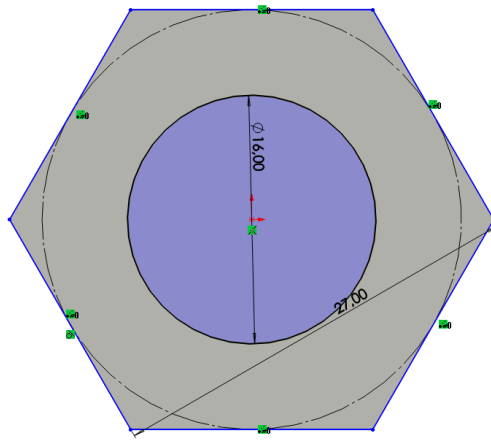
Эскиз детали «гайка в сборке с подшипником»
